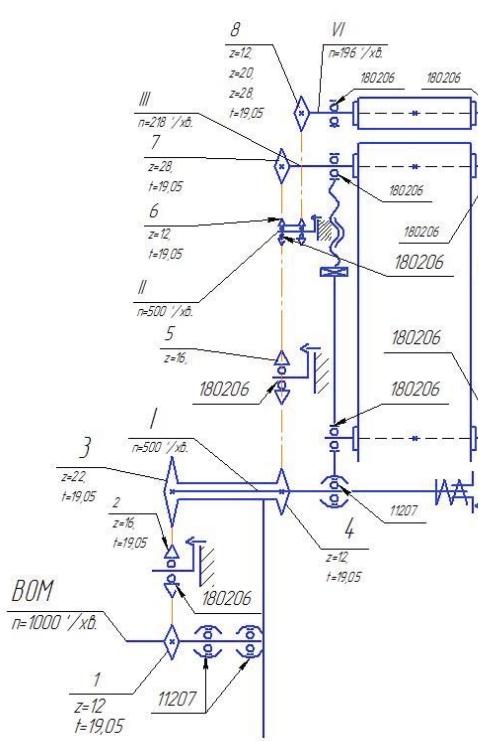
Кінематична схема приводу роторно-пальцевого робочого органу
